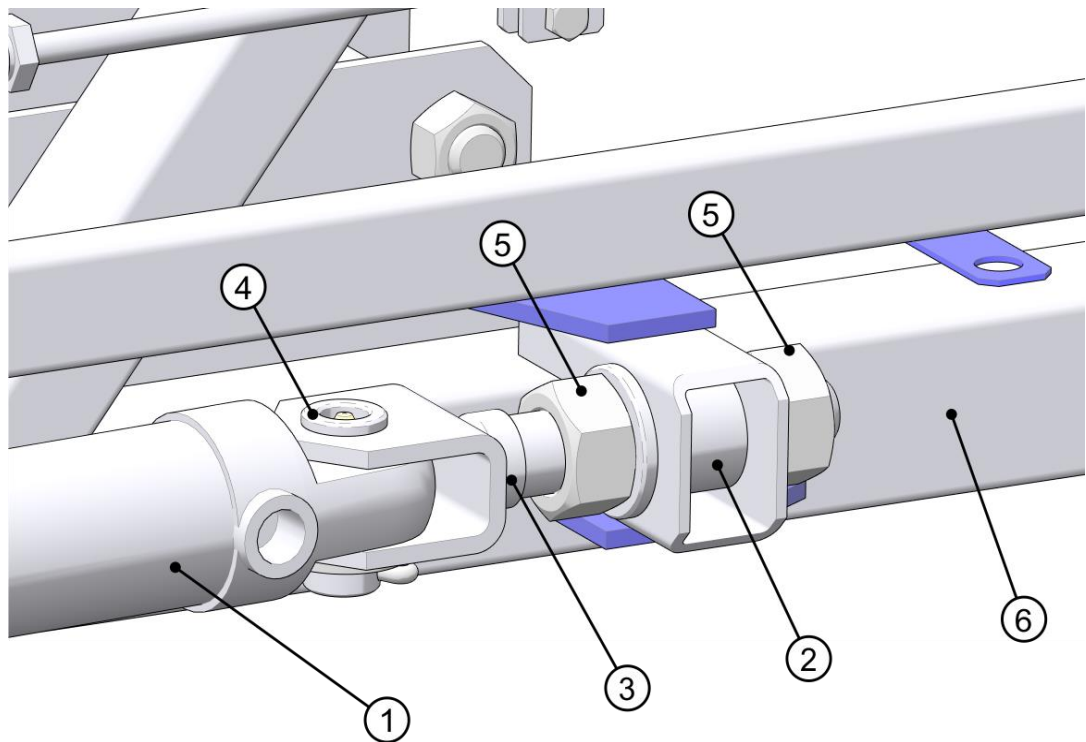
Элементы регулировки гидроцилиндра складывания штанги.
